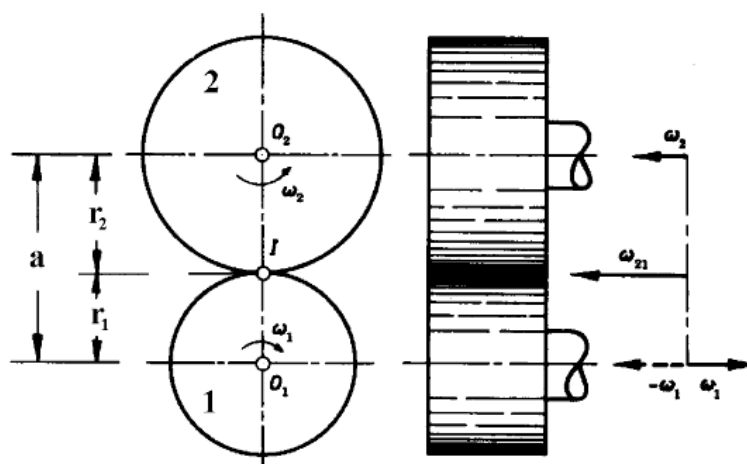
Axoides en un engranaje cilíndrico exterior
